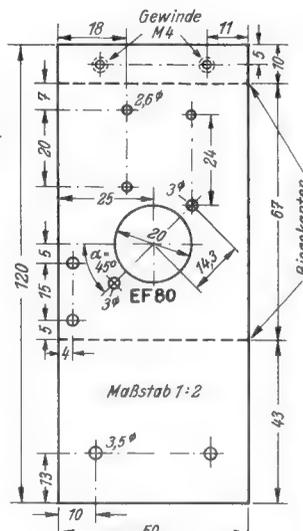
Maßskizze für das Chassis aus 2 mm starkem Aluminiumblech
